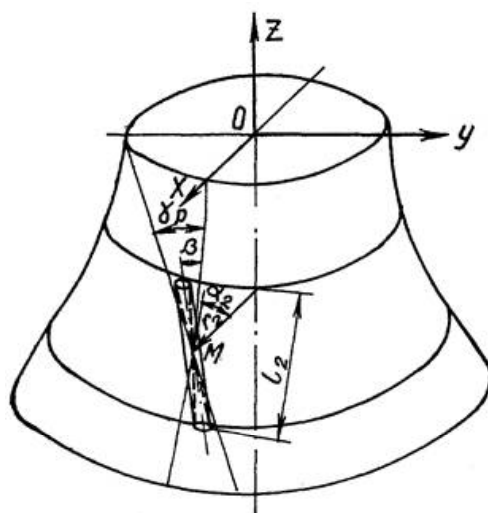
Схема перетворення конічної поверхні в гіперboloїд
